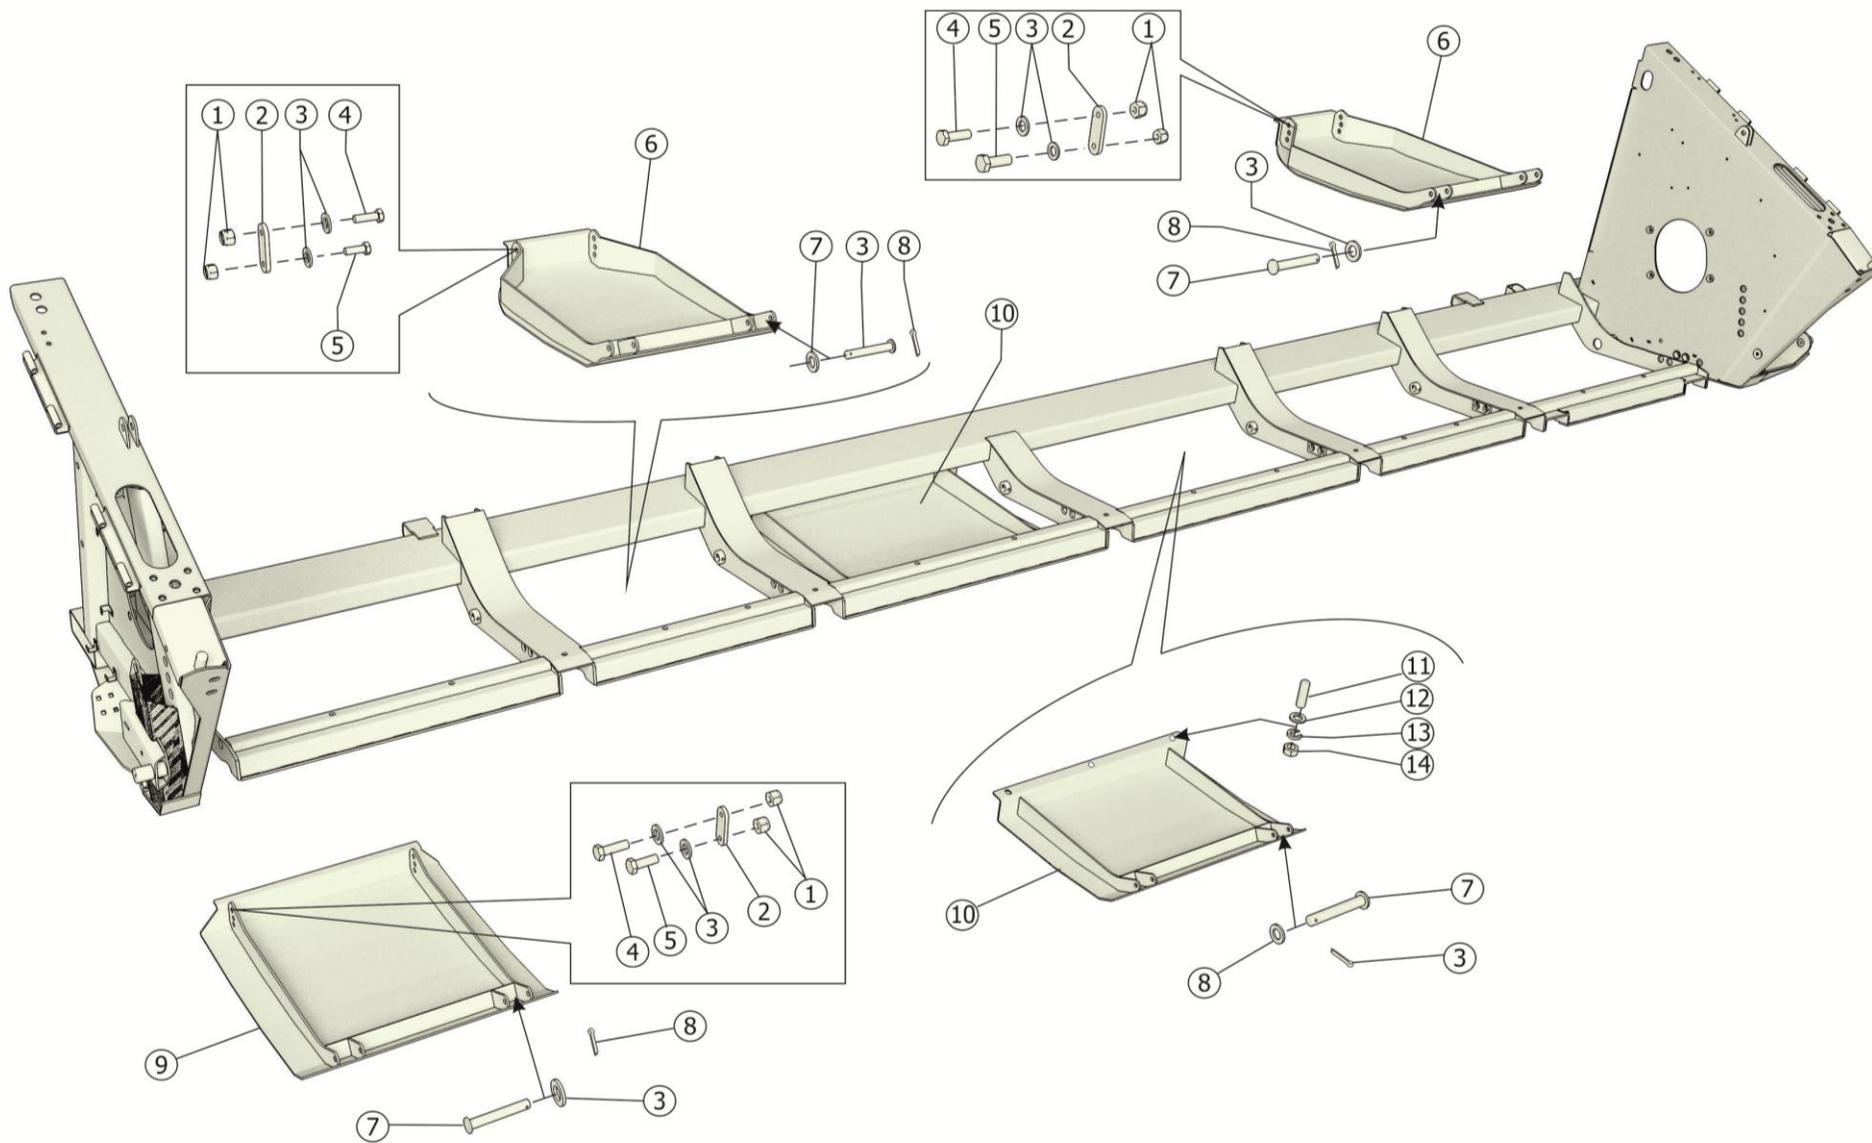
Установка башмаков ЖСУ-500.01.04.000
